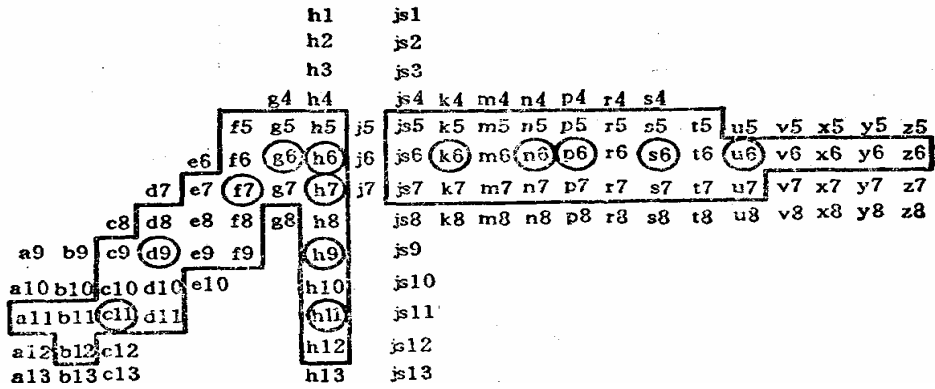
7 优先、常用和一般用途的轴公差带 (尺寸≤500mm)
